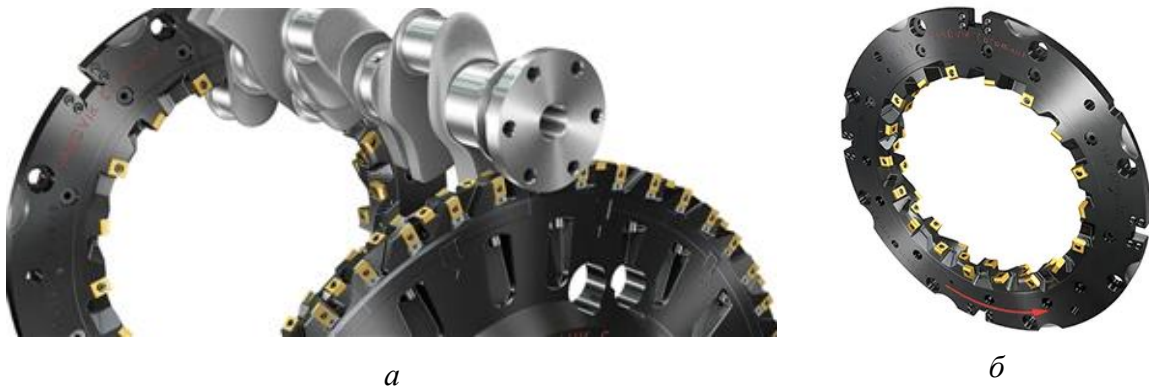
Фрезерування колінчастих валів (а) та фреза (б) [12]
